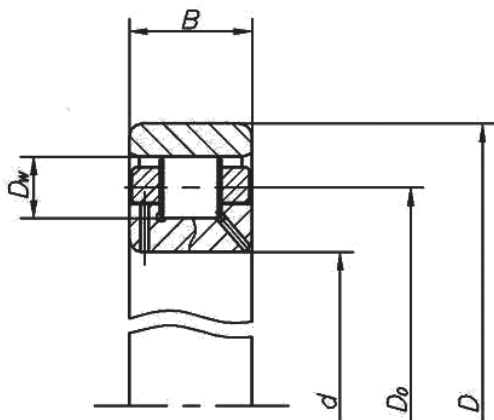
Радиальный роликоподшипник 5AB1002926P4: D_w — диаметр ролика, $D_w = 12$ мм; B — ширина подшипника, $B = 24$ мм; D_0 — диаметр окружности центров комплекта роликов, $D_0 = 155$ мм; d — внутренний диаметр подшипника, $d = 130$ мм; D — наружный диаметр подшипника, $D = 180$ мм
